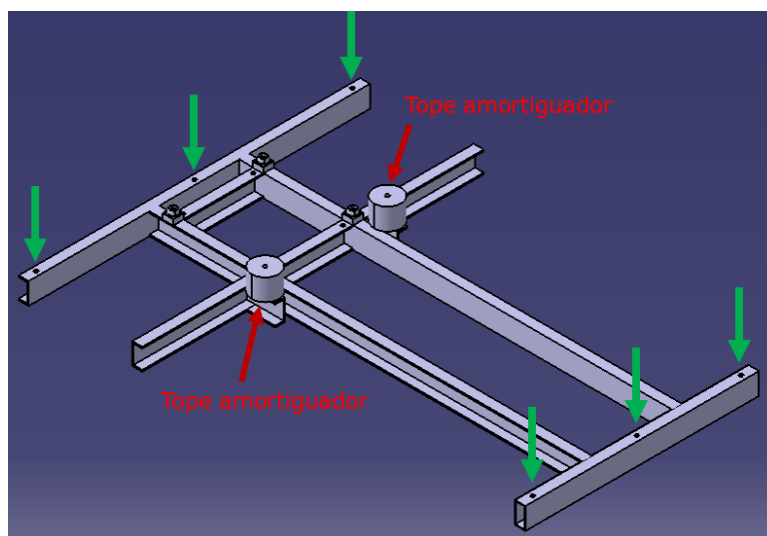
Fijación de la base a la zapata de hormigón y colocación del primer mástil
